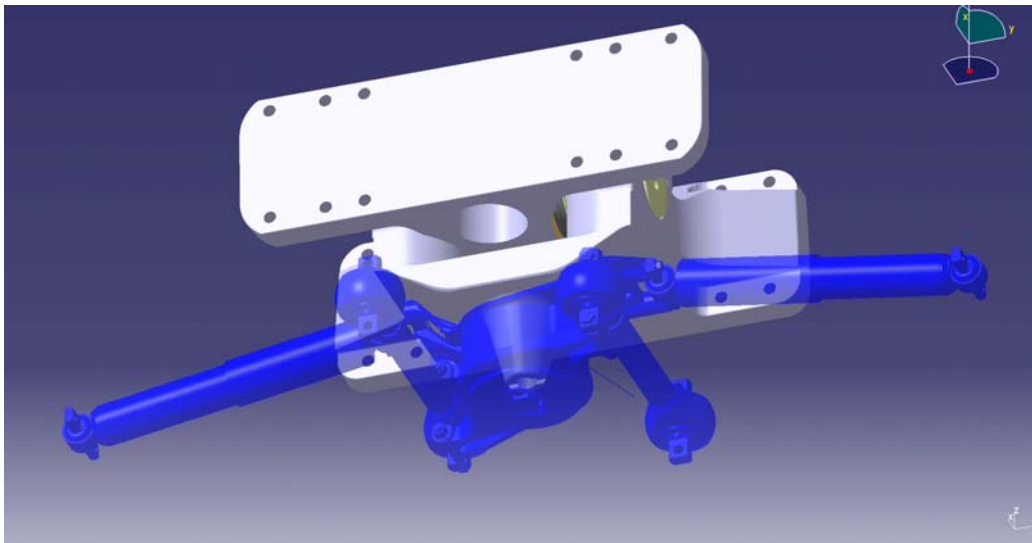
Am geschmiedeten Gelenkträger direkt integrierter Laufdrehgestell-Drehzapfen, auf welchen die Lemniskatenplatte mit Befestigung der Querdämpfer und Längslenker geschraubt wird
